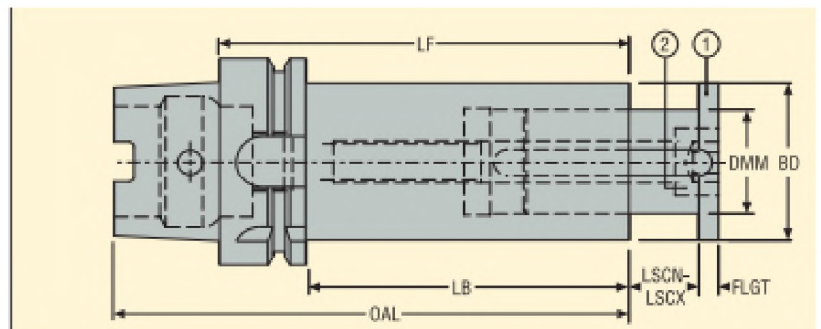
DM 5657 – Державка дискової фрези E9304565727120 [5, с.77]
